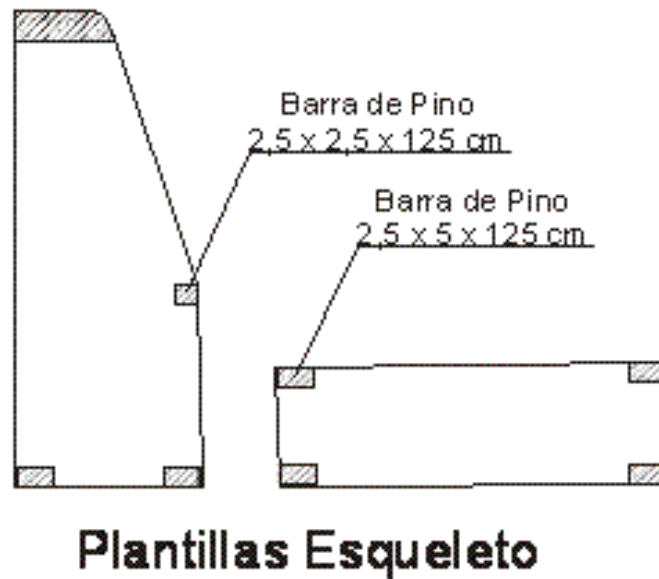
Posicionamiento de los puntos de ensamblaje en las plantillas
